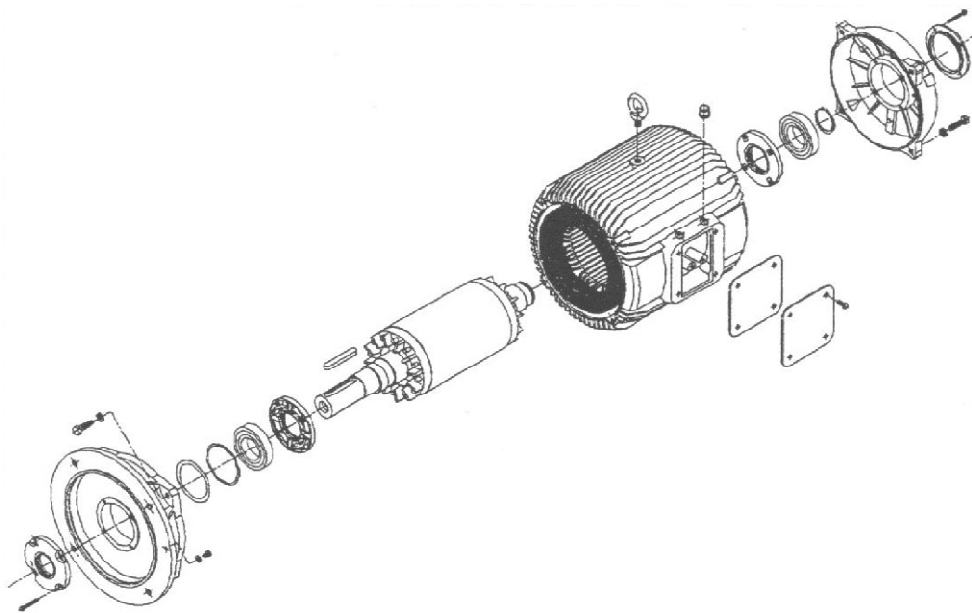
Despiece de un motor asíncrono trifásico con rotor de jaula de ardilla [2]
